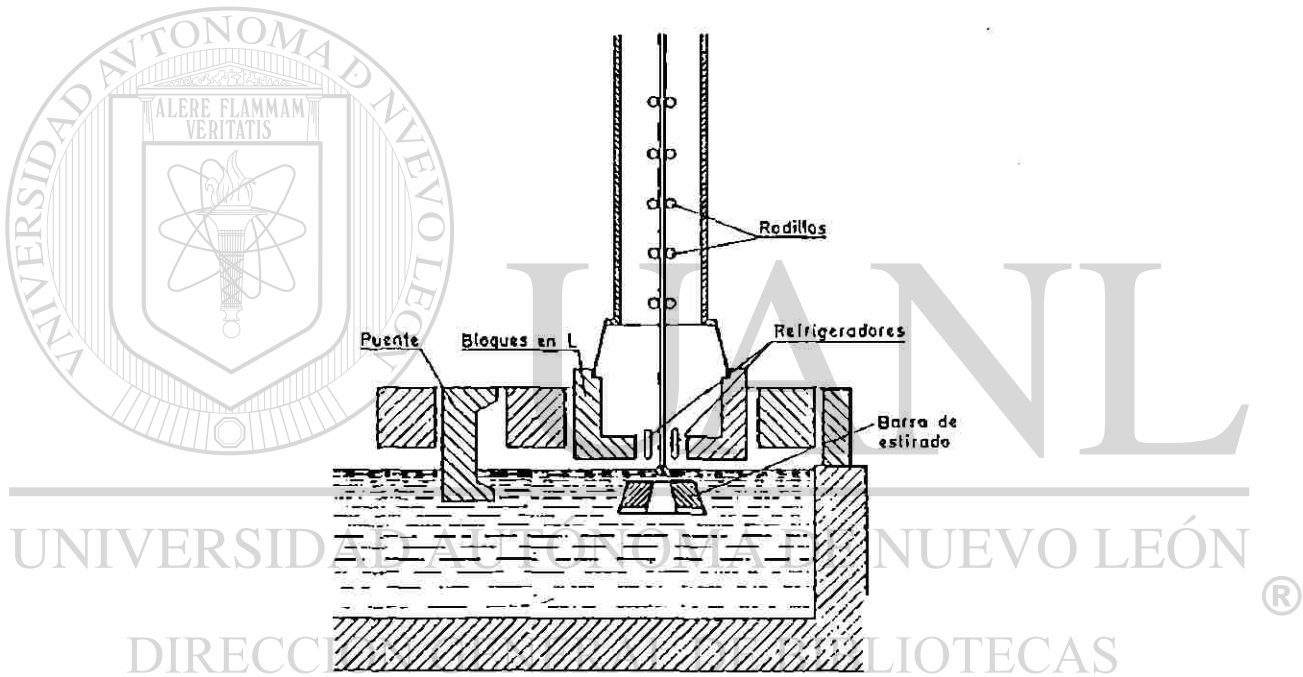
Sistema Pittsburgh de estirado de vidrio plano.
